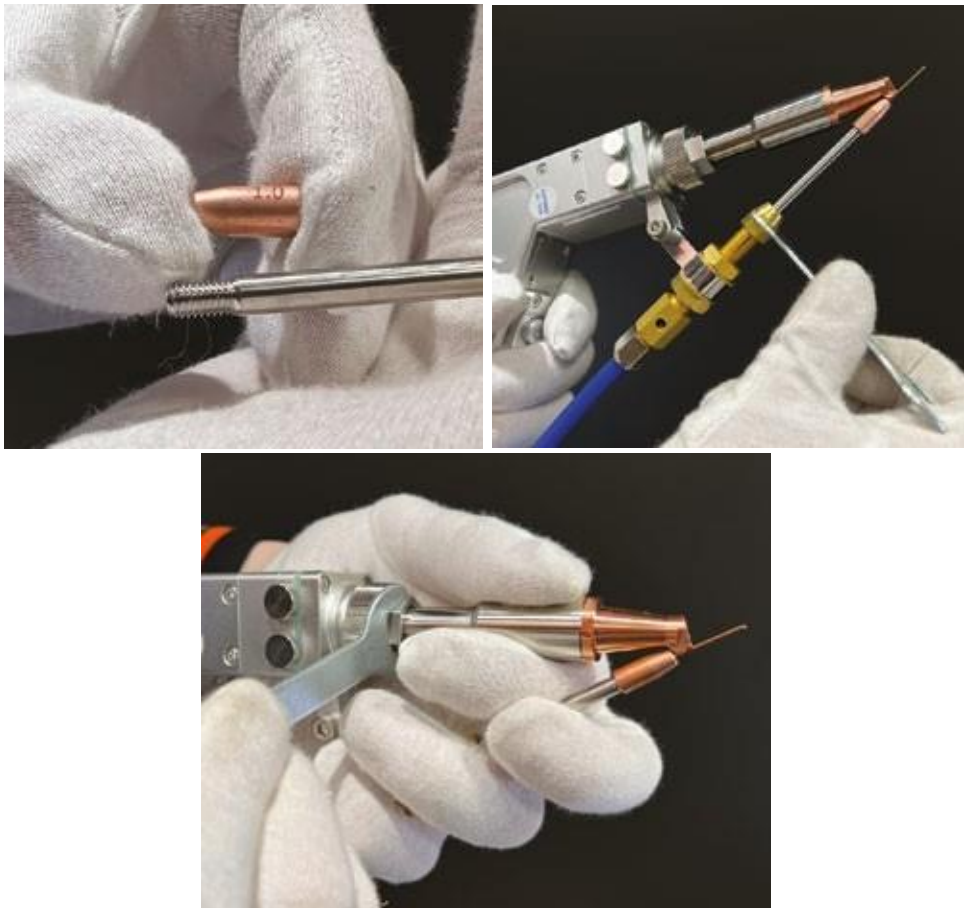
Установка телескопической втулки с наружной резьбой на сварочную головку.
